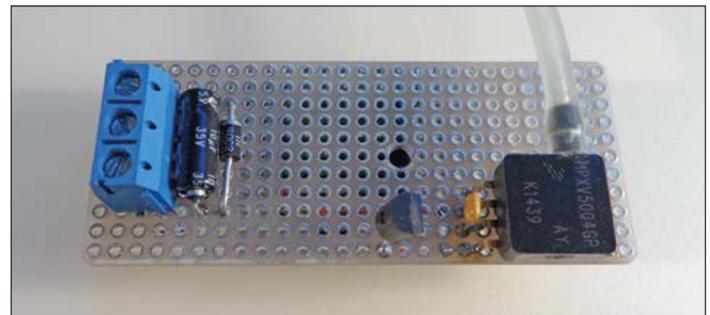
Die Wandlerschaltung auf einem Stück Experimentierplatine.
